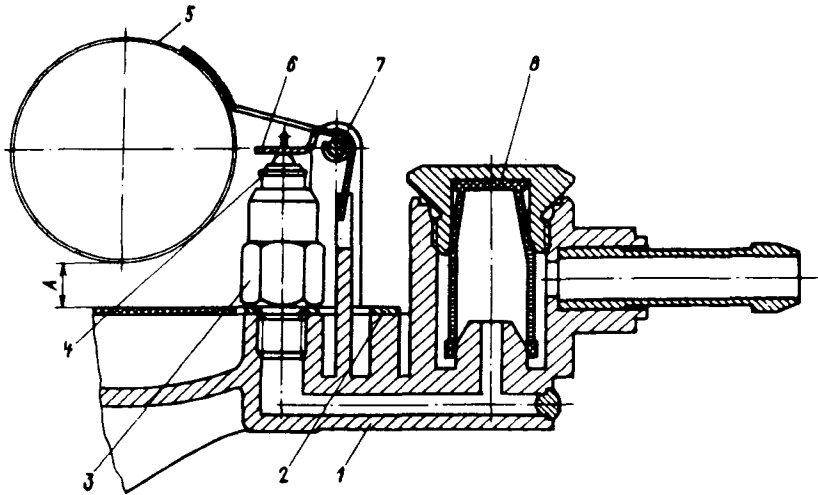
Конструкция на механизма за поддържане на постоянно ниво на горивото: 1 – капак на карбуратора; 2 – гарнитура; 3 – корпус на клапана; 4 – клапанна игла; 5 – поплавък; 6 – езице; 7 – ос на поплавък; 8 – филтриращ елемент
